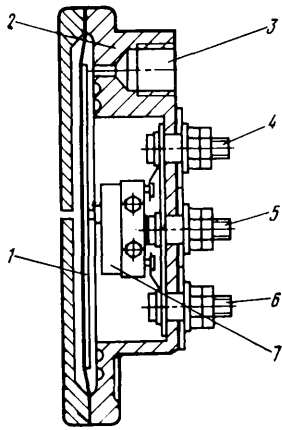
Электровакuumный выключатель фирмы Энсайд (США): 1 — диафрагма с пластиной; 2 — корпус; 3 — вакуумная полость; 4 — клемма для подключения цепи управления стартером; 5 — клемма для цепи зажигания; 6 — клемма для цепи электромагнита; 7 — микровыключатель
